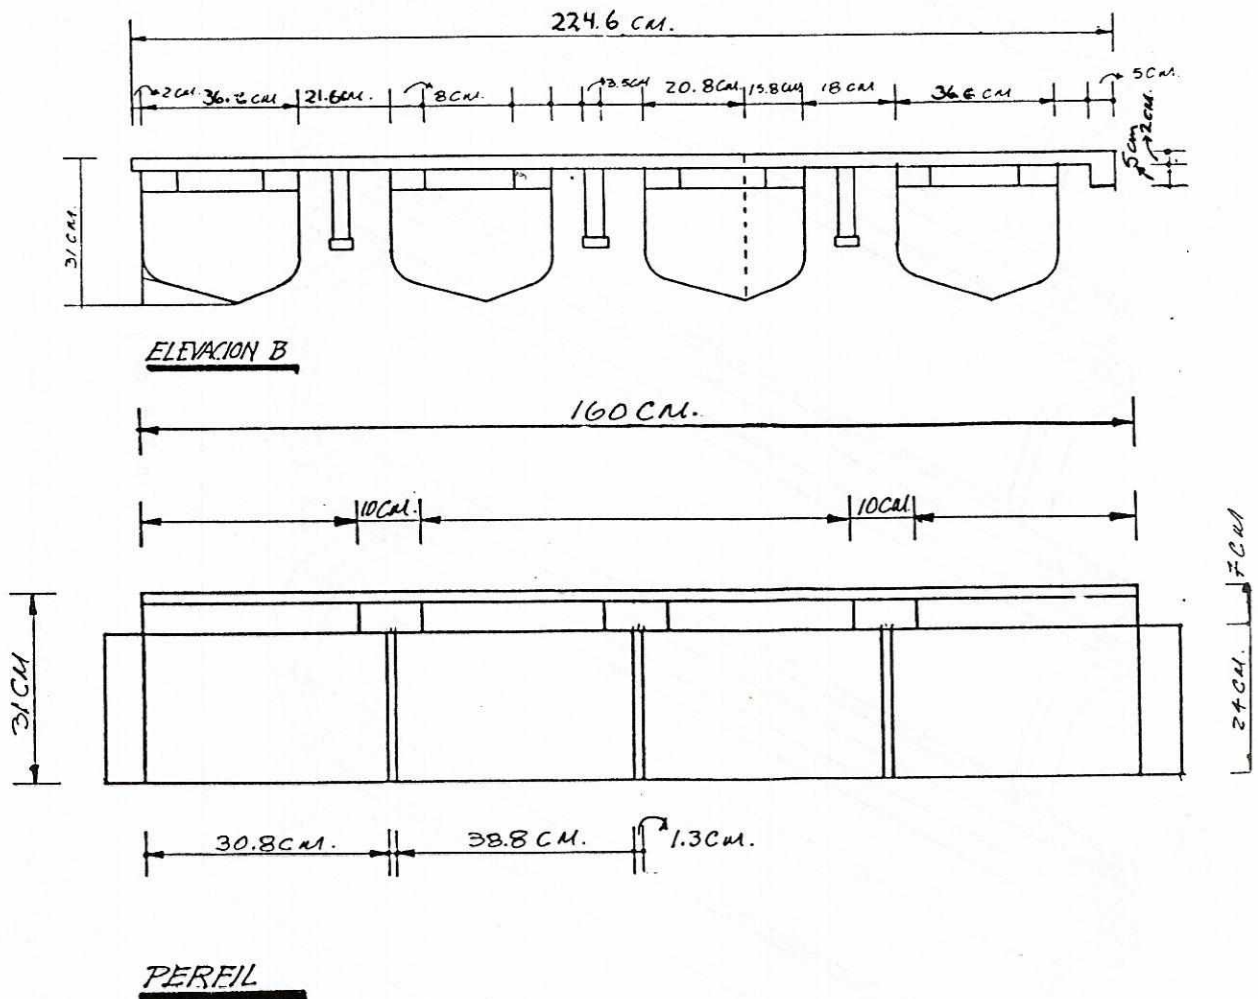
Dimensiones y diseño de contramolde para canaleta
